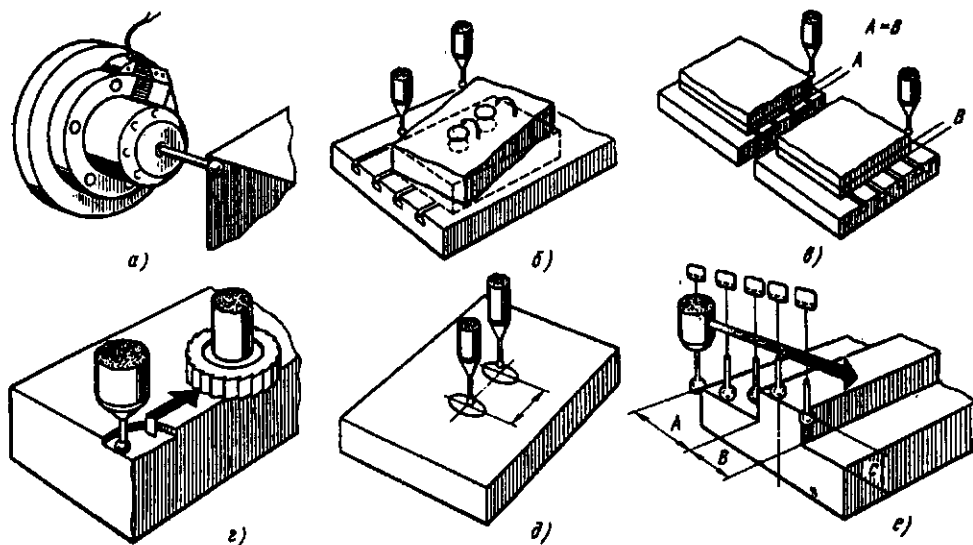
Схемы применения щупов на сверлильно-фрезерно-расточном станке с ЧПУ для измерения: а – установки нулевой точки; б – погрешности установки заготовки на столе; в – снимаемого припуска; г – припуска на чистой переход; д – межосевого расстояния; е – обработанной детали
